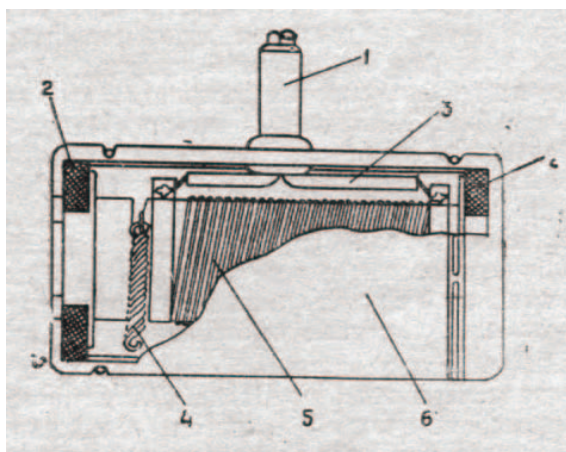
Схема электрического подогревателя для йодной трубки: 1 – втулка; 2 – прокладка; 3 – провод сетевой двухжильный; 4 – пружина; 5 – обмотка; 6 – корпус
